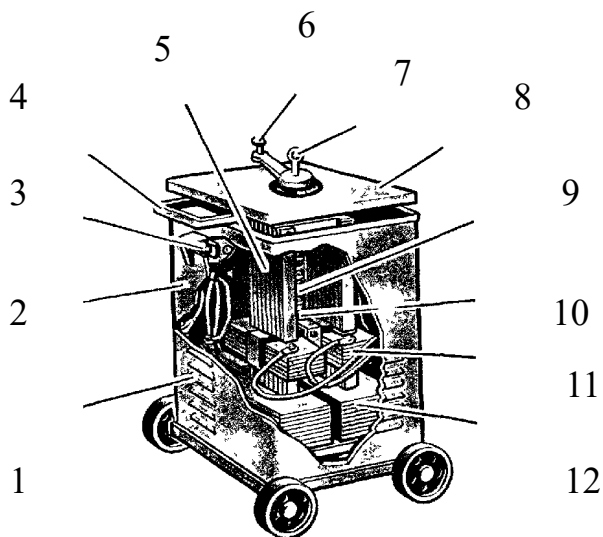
Зварювальний трансформатор: 1 - жалюзі для охолодження; 2 - корпус; 3 - затискач для приєднання проводів зварювального дроту; 4 - ручка; 5 - замкнутий магнітопровід (сердечник); 6 - рукоятка; 7 - рем-болт; 8 - кришка корпусу; 9 - вертикальний гвинт; 10 - ходова гайка гвинта; 11 - вторинна обмотка трансформатора; 12 - первинна обмотка трансформатора
